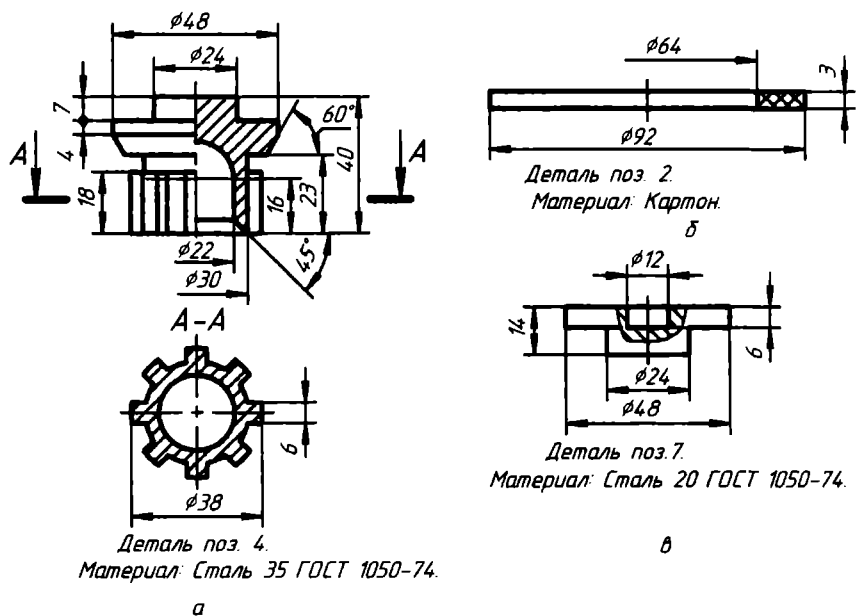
Чертежи: а — клапана; б — прокладки; в — тарелки
